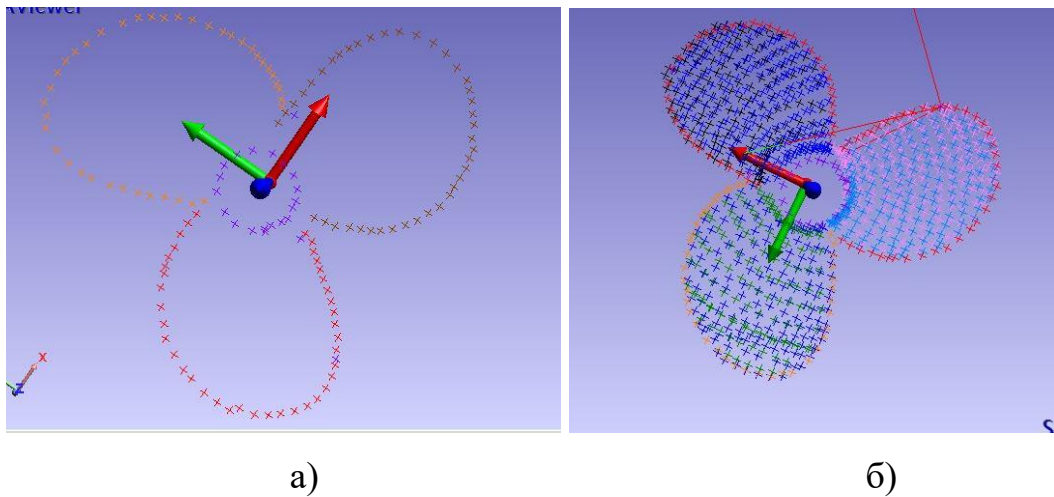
Вихідна 3D-модель заготовки 3-х лопастевого ГВ: а) координати кромки і торця; б) 3D-модель заготовки
